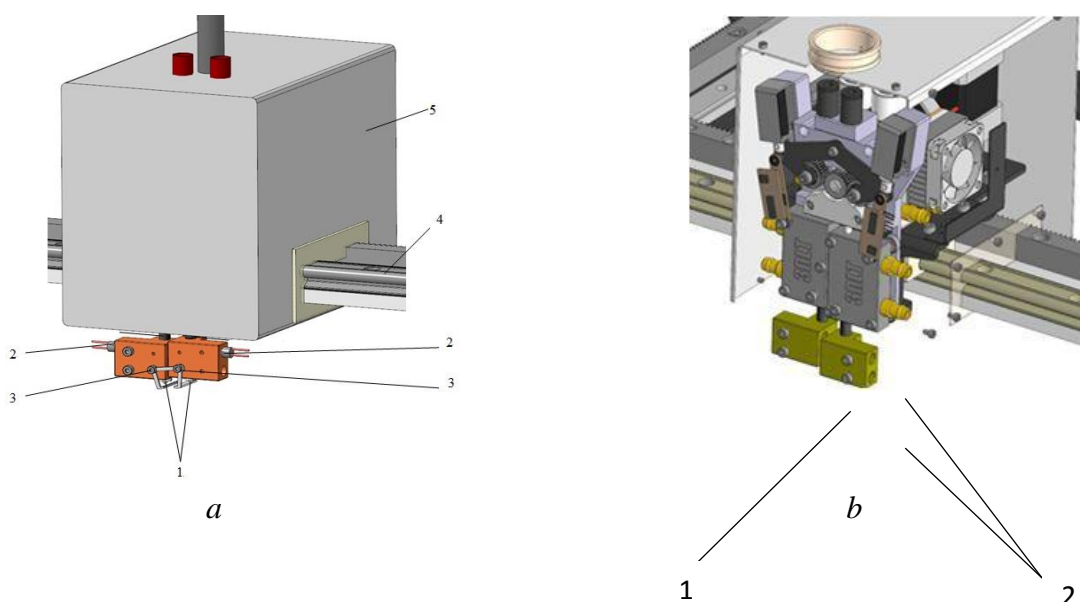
Экструзионный блок в термоизолирующем корпусе: *a* – вид в сборе: 1 – сопла, 2 – нагревательные элементы; 3 – клапан; 4 – рельсовая направляющая; 5 – термоизолирующий корпус; *b* – вид без передней стенки: 1 – водоблок смещения, 2 – фитинги
